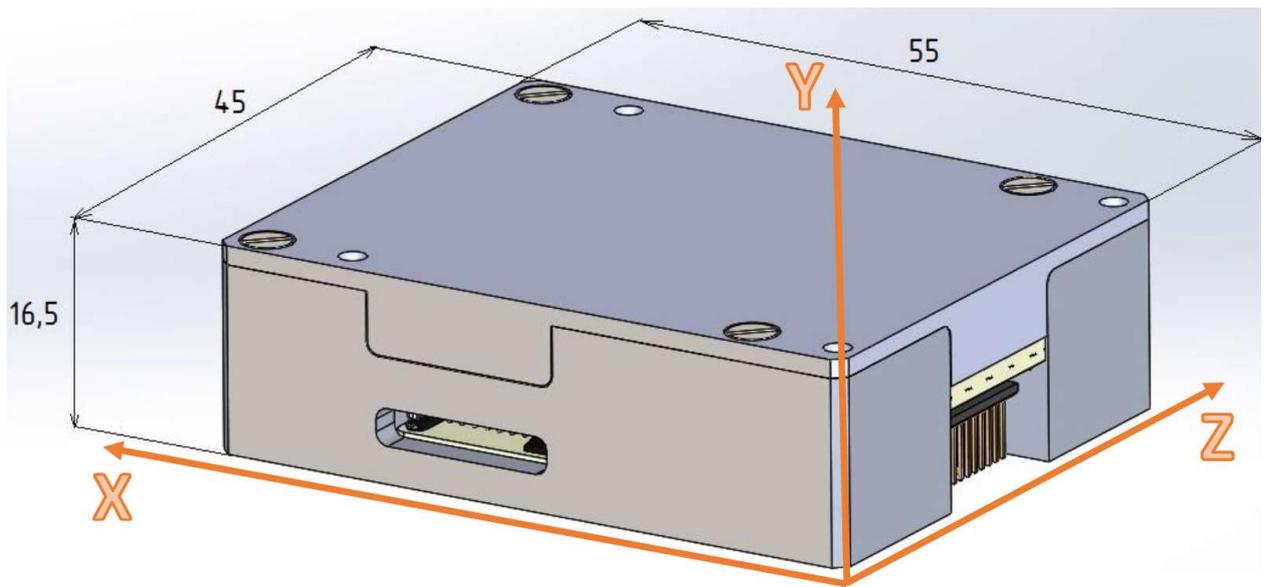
Внешний вид и габаритные размеры изделия
